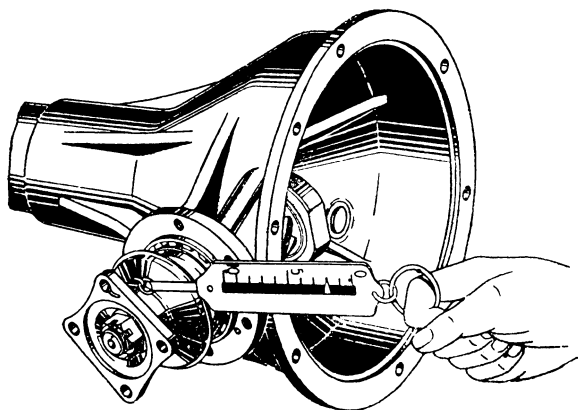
Проверка затяжки подшипников ведущей шестерни.
